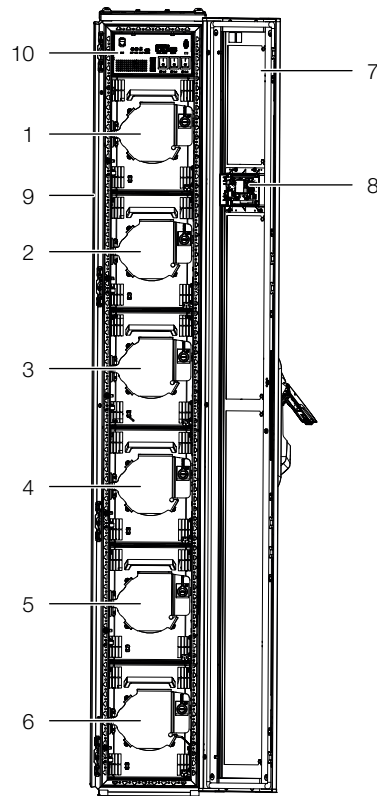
Parte frontal del Liquid Cooling Package – puerta frontal abierta
